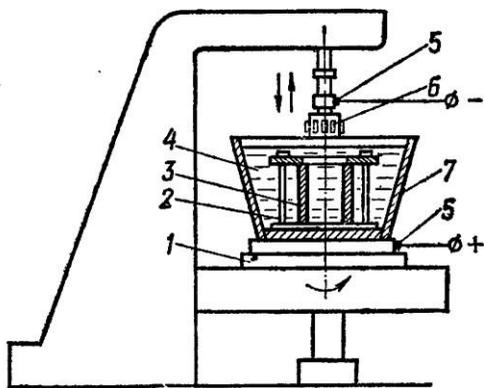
Схема верстата для електрохімікомеханічного хонінгування
